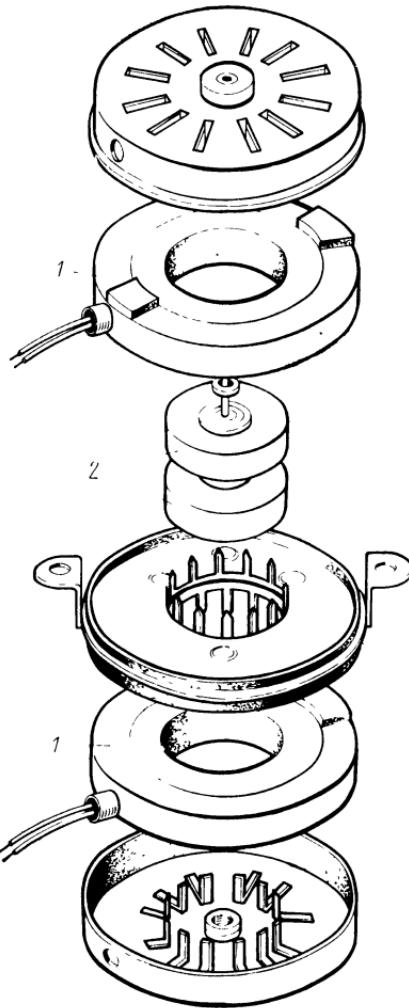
Конструкция двойного синхронного двигателя «Валво AU5050»:
